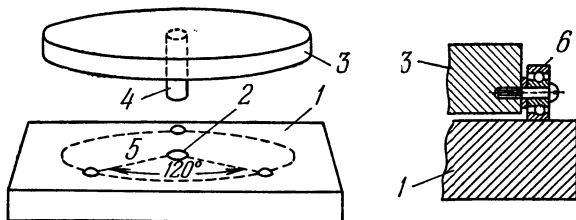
Станочек для шлифовки и полировки зеркал. 1—доска-основание, 2—отверстие для оси столика, 3—вращающийся столик, 4—ось столика, 5—стальные шарики, 6—шарикоподшипник.
